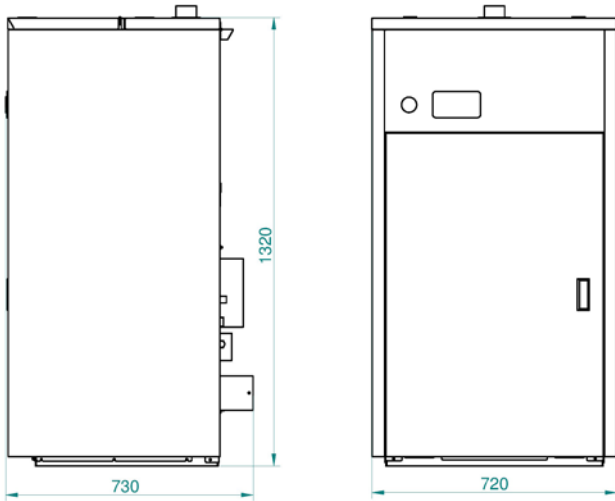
NARA PL. 24-34 - dimensioni di ingombro - overall dimensions -
